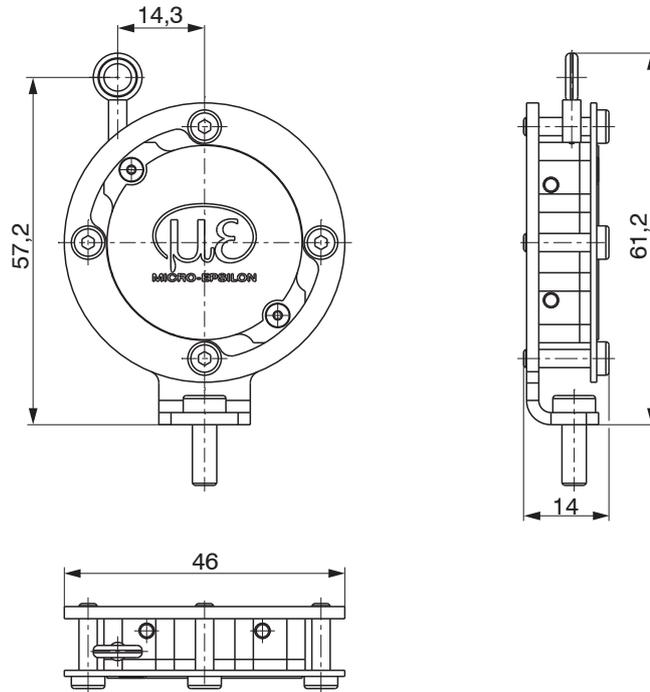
Maßzeichnung WDS-MB33 Montagewinkelset - Seitenansicht, Abmessungen in mm
